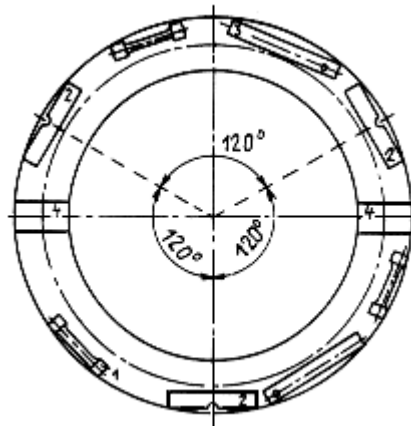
Схема вырезки образцов из трубы паропровода: 1 - образцы для испытания на растяжение; 2 - образцы для испытания на ударную вязкость; 3 - образцы для карбидного анализа; 4 - образцы для металлографических исследований
